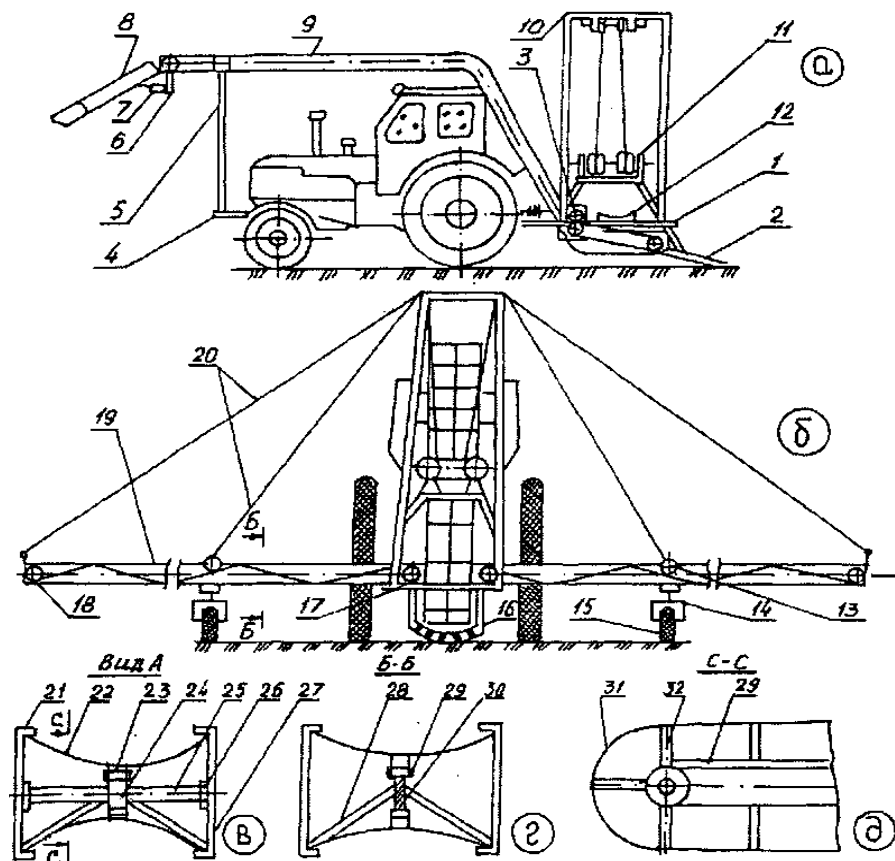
Агрегат для выборочной уборки плодов: 1 – опорная рама; 2 – лоток; 3 – редуктор; 4 – балка; 5, 10 – стойка; 6 – упор; 7 – гидроцилиндр; 8 – укладчик; 9 – погрузочный транспортер; 11 – лебедка; 12 – транспортеры боковые; 13 – шарнир; 14 – опорная стойка; 15 – опорное колесо; 16 – эластичный материал; 17 – шарнирно-поворотное крепление; 18 – натяжные звездочки; 19 – ферма; 21 – боковины; 22 – лотковый транспортер; 23 – приводная цепь; 24 – натяжное устройство; 25 – вал; 26 – подшипники; 27 – несущая ферма; 28 –
